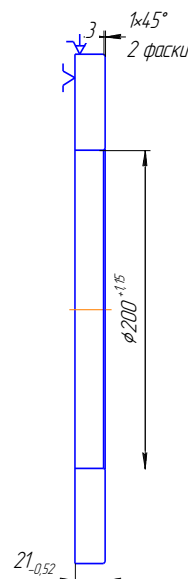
Схема установки заготовки для токарно-винторезной операции 005
